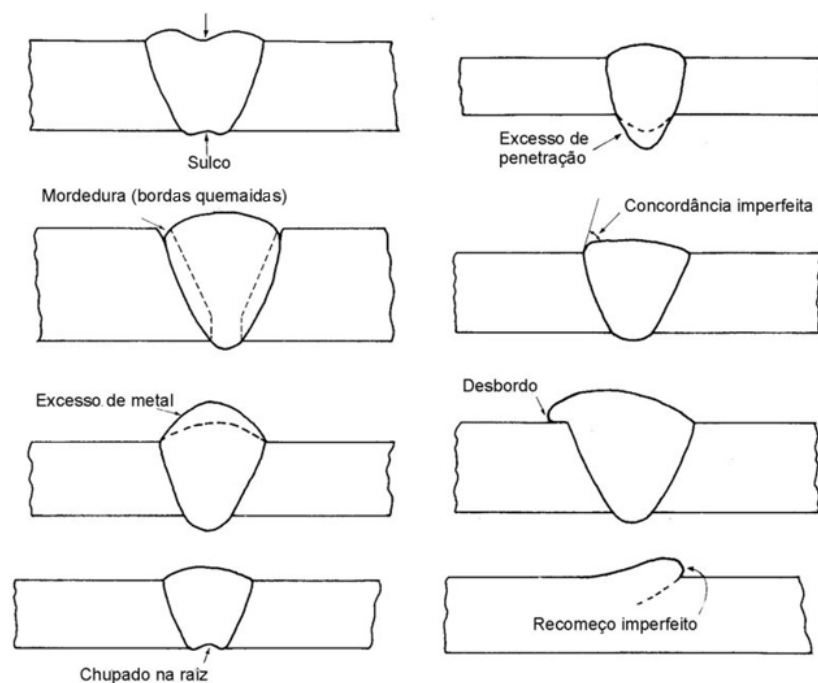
Defeitos de forma mais importantes nas juntas soldadas de topo[44].
